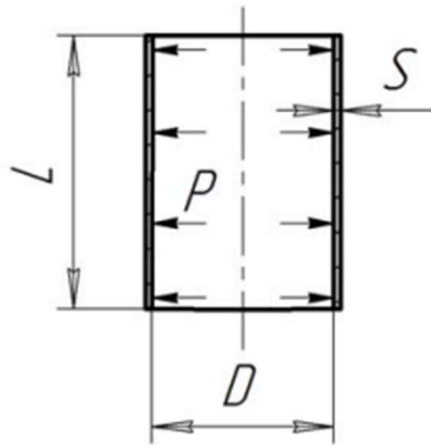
Розрахункова схема для визначення товщини циліндричної обичайки
